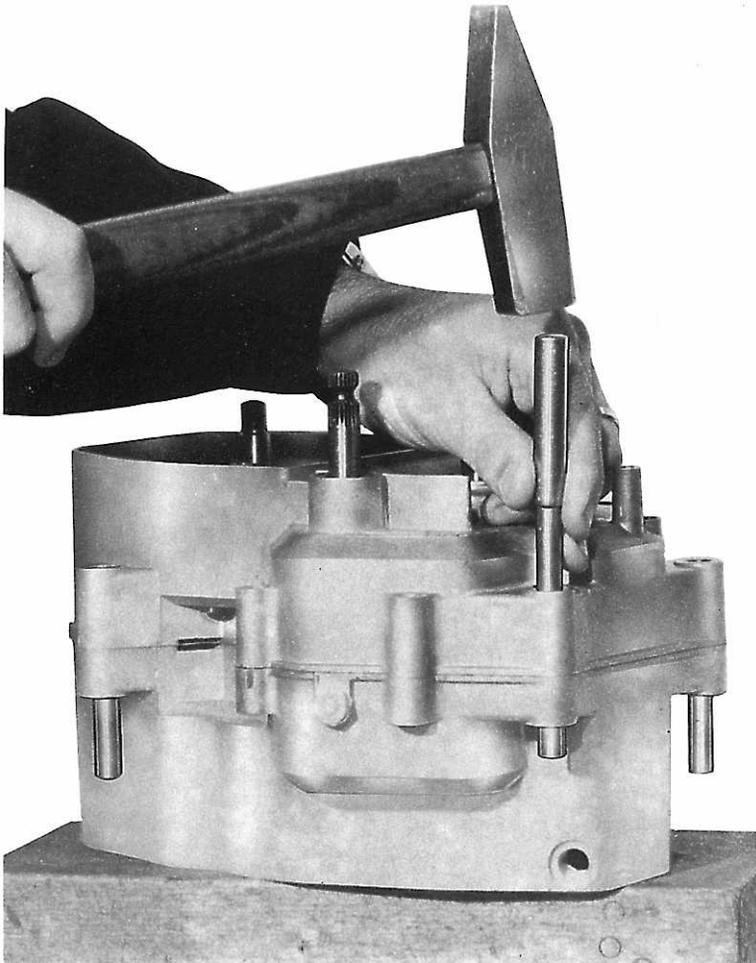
Ausbau der Gehäusehälfte-Befestigungsschrauben
